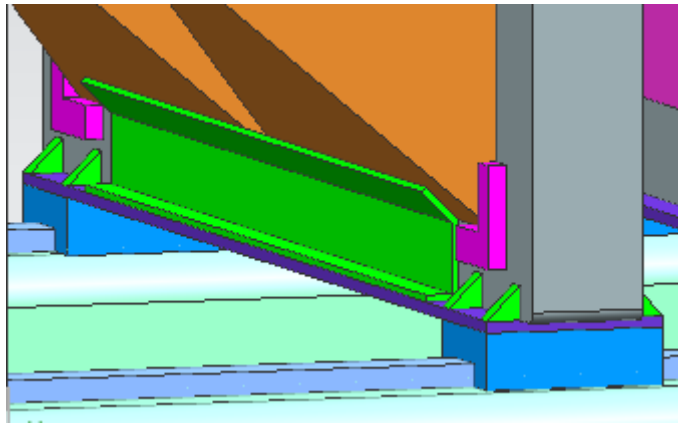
Otra vista del conjunto placa móvil (lado izquierdo)
